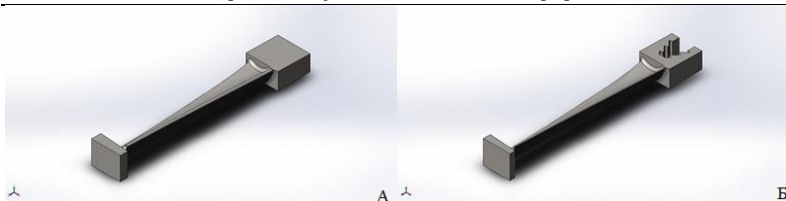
3D моделі: А – заготовка, Б – лопатка.
